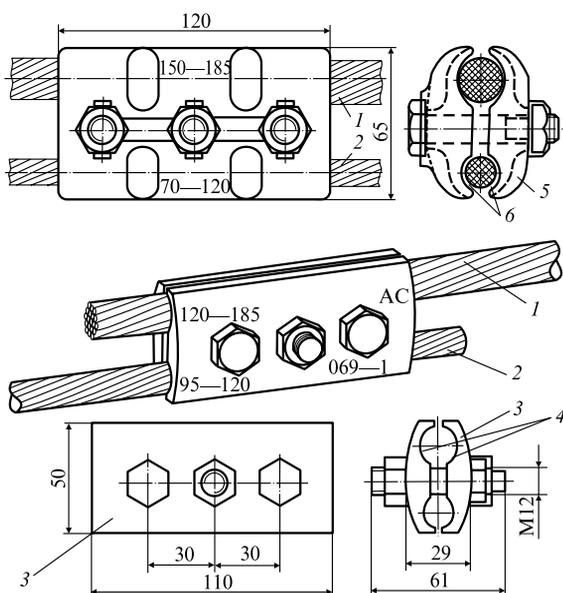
Переходной зажим ПАМ: 1 и 2 — алюминиевый (сталеалюминиевый) и медный провода; 3 — медный зажим; 4 — алюминиевое напыление; 5 — алюминиевый зажим; 6 — медная пластина из ленты (припаивается)
